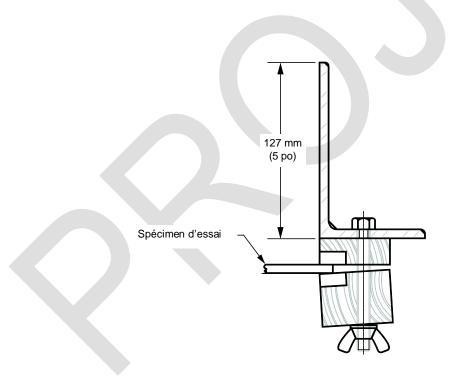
Détail de la coupe A-A — Spécimen d'essai incorrectement fixé [>3 mm (1/8 po)]
